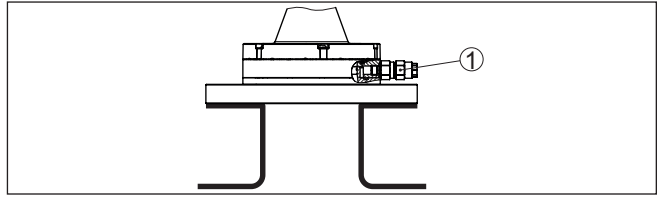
Antena de plástico tipo corneta com flange adaptador
